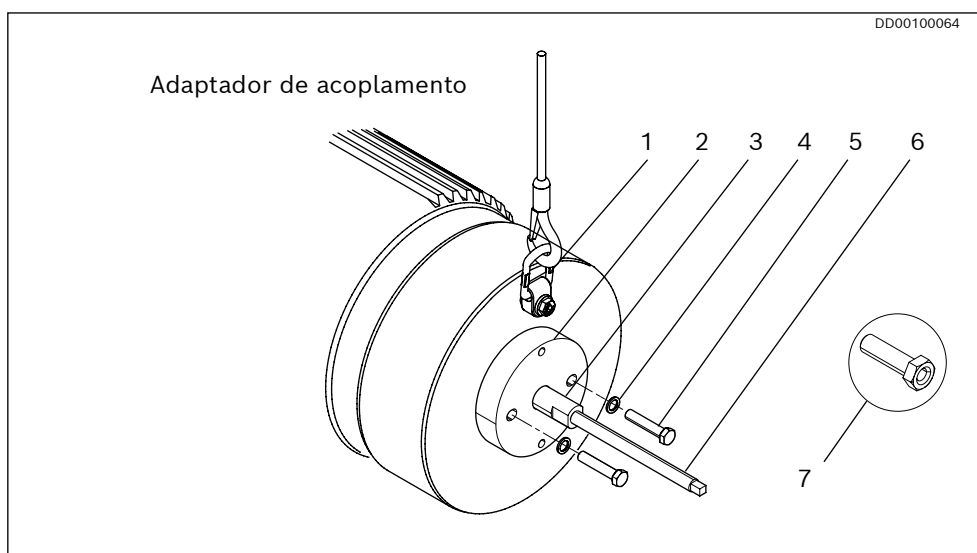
Ferramenta de montagem para a remoção do adaptador de acoplamento
